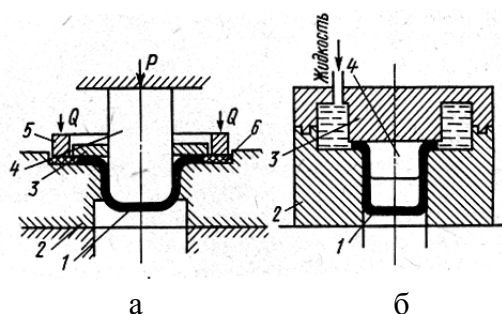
Устройство для вытяжки с дополнительным нагружением в радиальном направлении:
